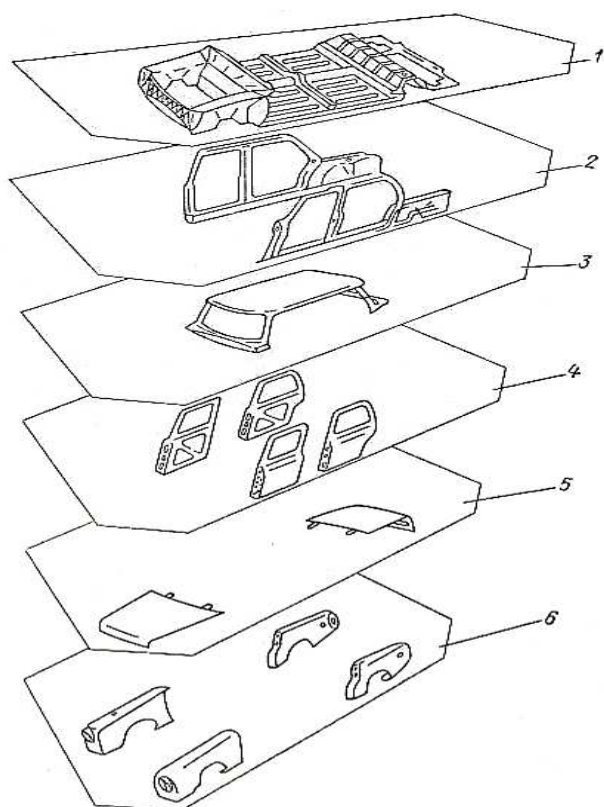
Общая схема последовательности сборки-сварки кузова легкового автомобиля:
